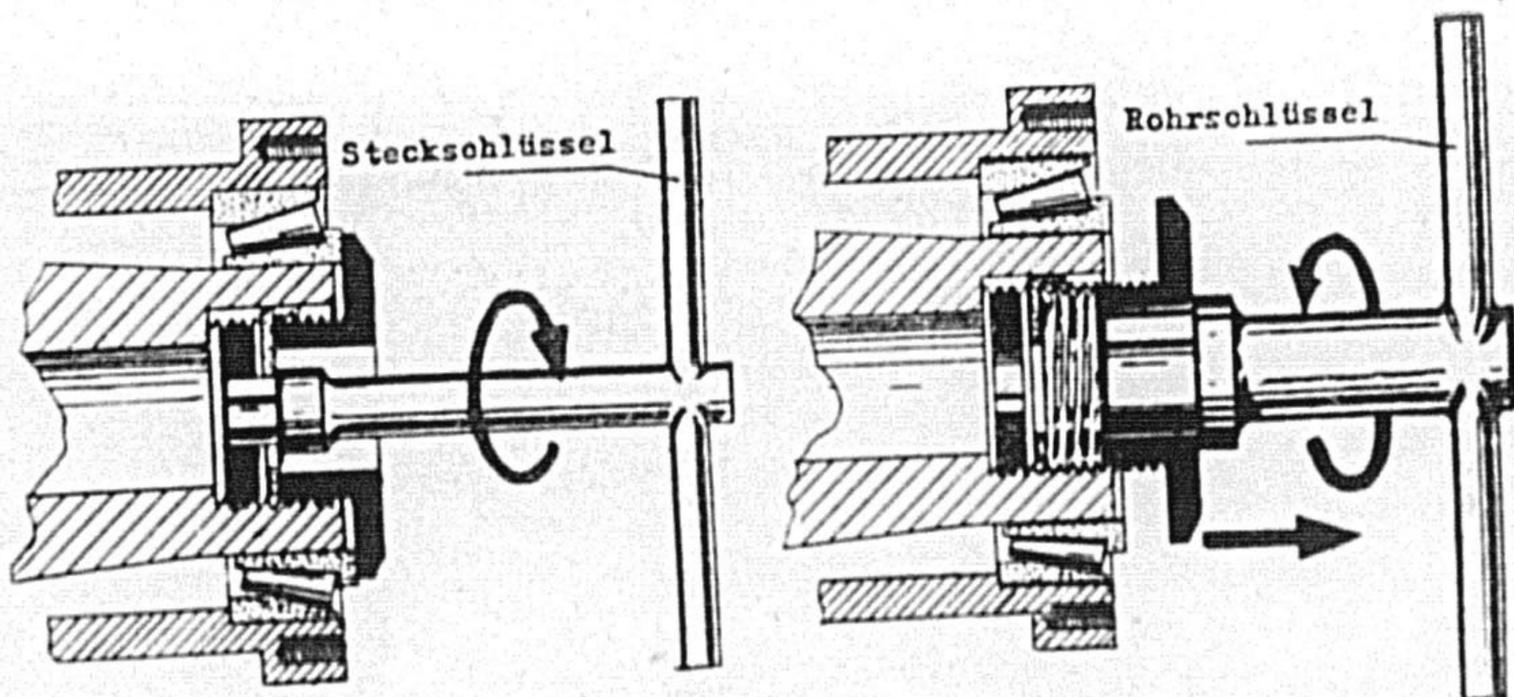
Lösen der inneren Gegenmutter und Abschrauben der großen Haltemutter
